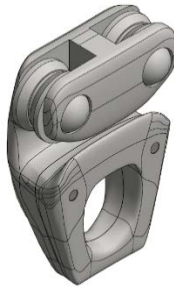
Dispositif d'ancrage, type : ABS-Lock® SYS III monté sur des points d'ancrage individuels absorbant les forces avec guide Ø 6 mm
